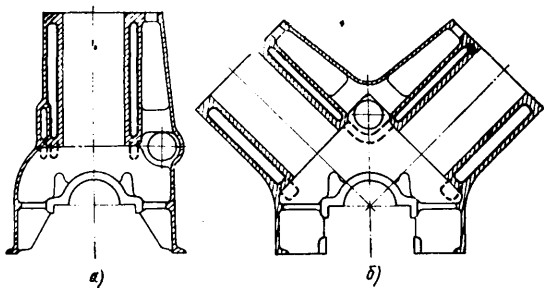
Поперечный разрез блока цилиндров рядного (а) и V-образного (б) двигателей
